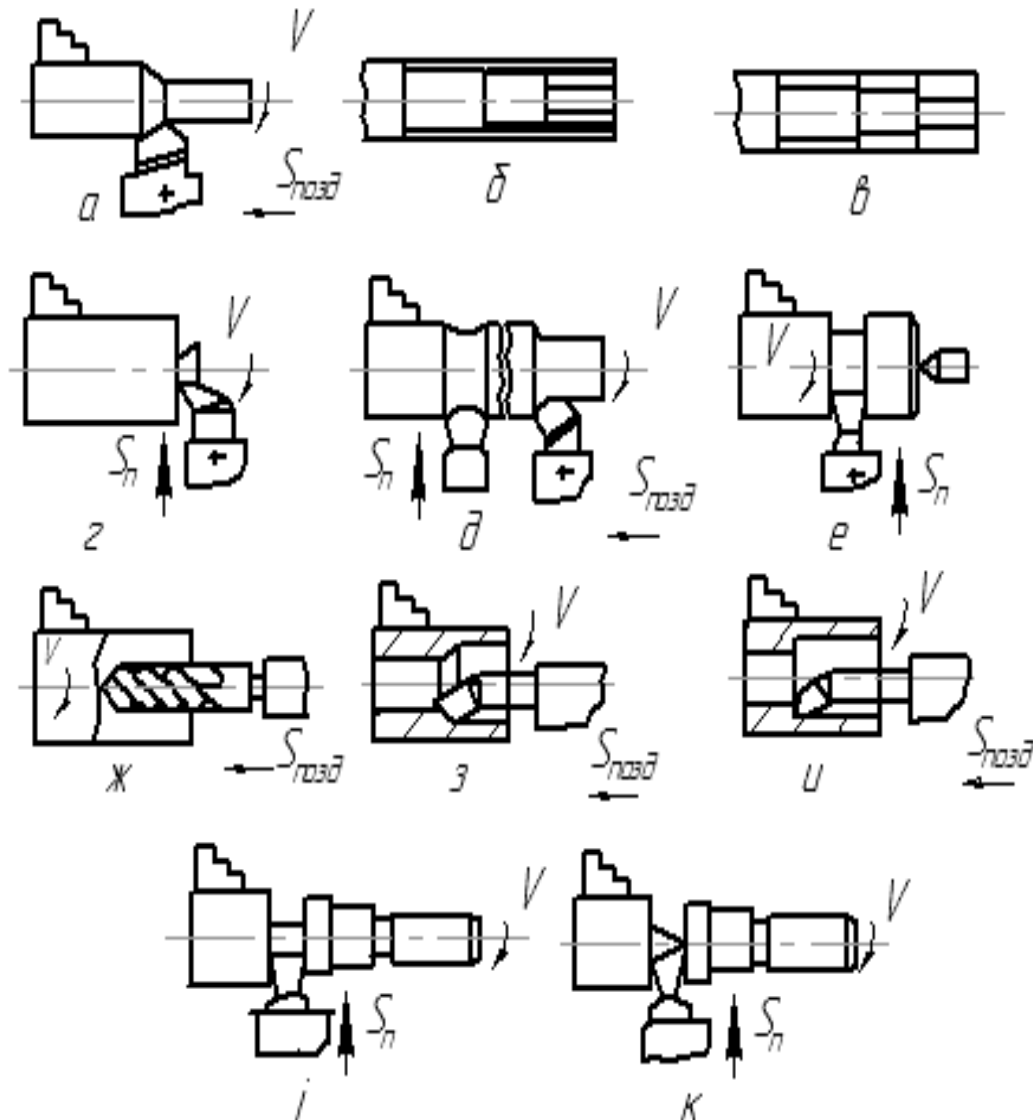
Схеми обробки заготовок на токарно-гвинторізних верстатах
